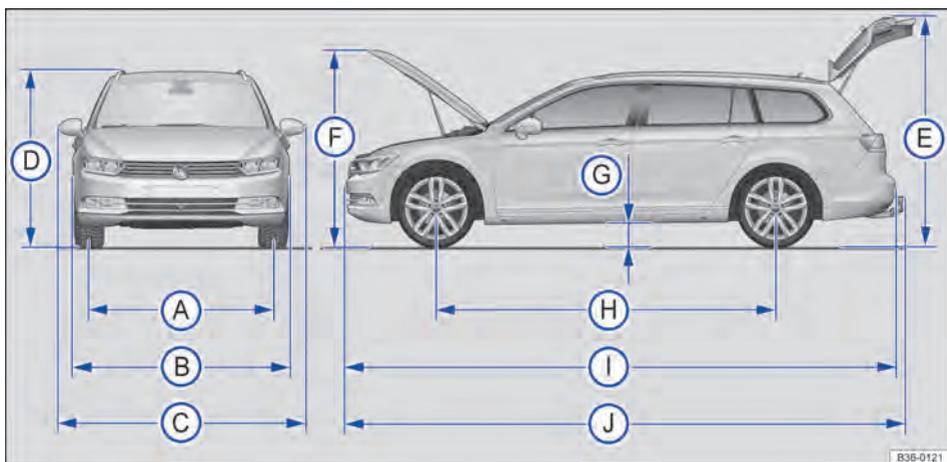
Dimensões (Passat Variant e Passat Alltrack).
